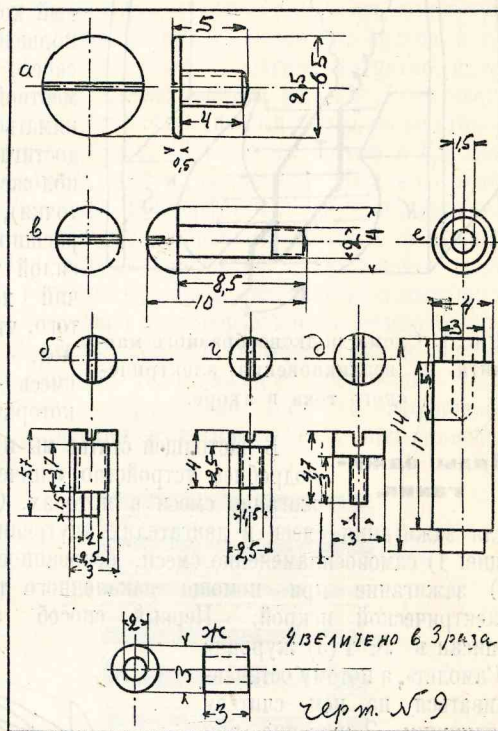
а — стопорный винт кривошипа; б — палец кривошипа; в — стопорный винт вала; г — прижимный винт шайбы пошня; д — винт соединения отъемного диска со стойками основного; е — стойка-распорка дисков; ж — вкладыш поршневого пальца.
